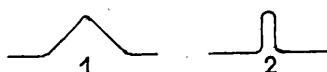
1 : en cours de bobinage ; 2 : prise resserrée pour finition.
